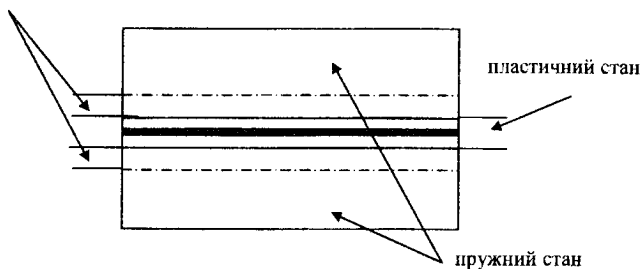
Деформівний стан металу різних зон зварного з'єднання
